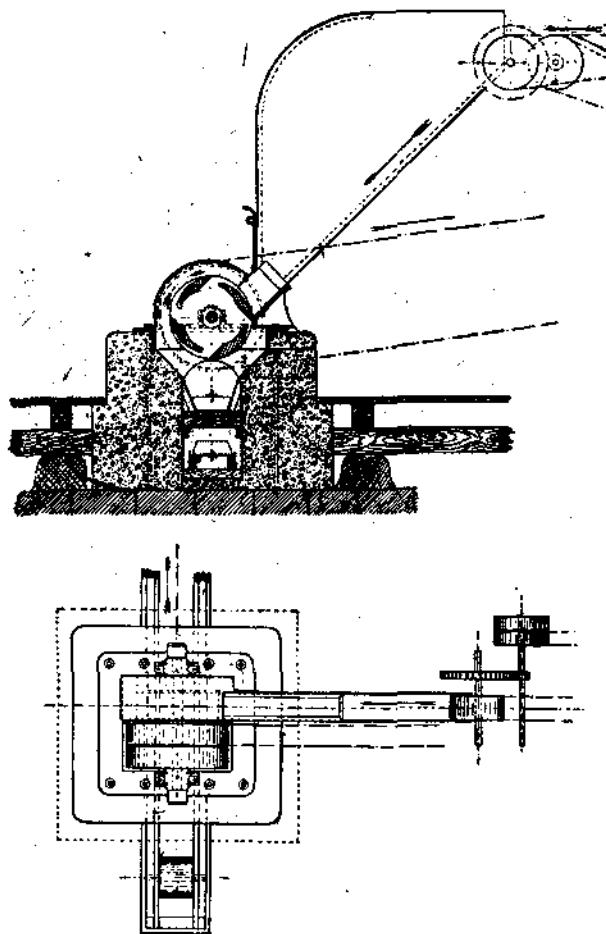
Дробильный станок на бетонном фундаменте. Боковой вид и план.
